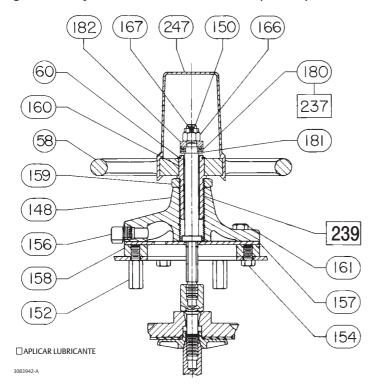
Conjunto de volante montado en la parte superior para actuadores tamaños 45 - 76
